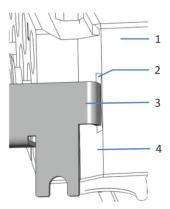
Entfernen der Hinterspülplatte mit dem Abstandswerkzeug
